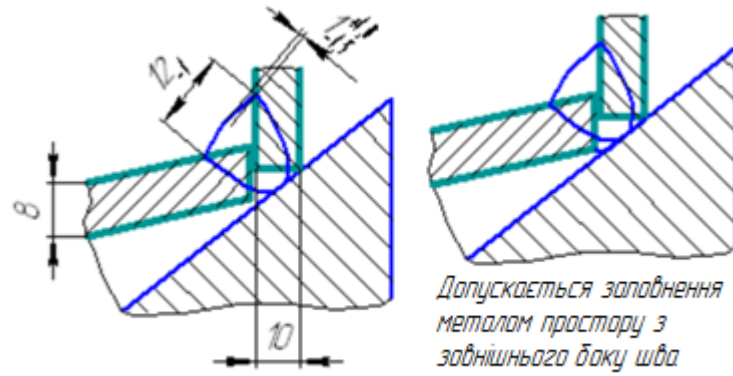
Ескіз зварного шва. Геометричні параметри
